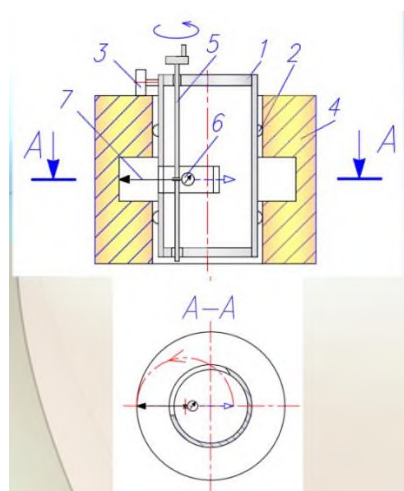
Пристрій для контролю радіуса внутрішніх циліндричних поверхонь.
